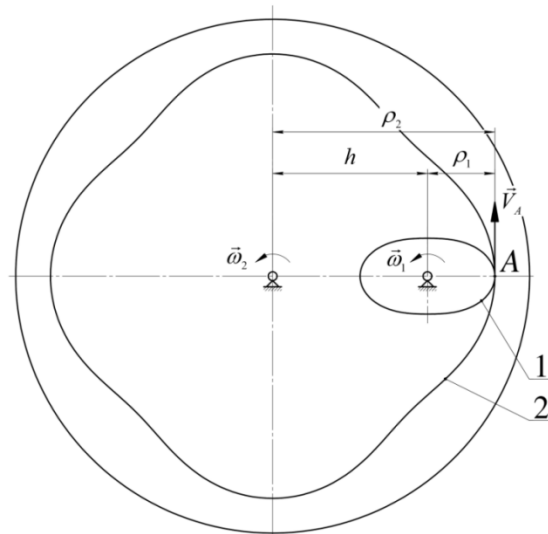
Расчетная схема пары зубчатых колес: 1 — овальное зубчатое колесо с внешними зубьями, 2 — некруглое зубчатое колесо с внутренними зубьями
